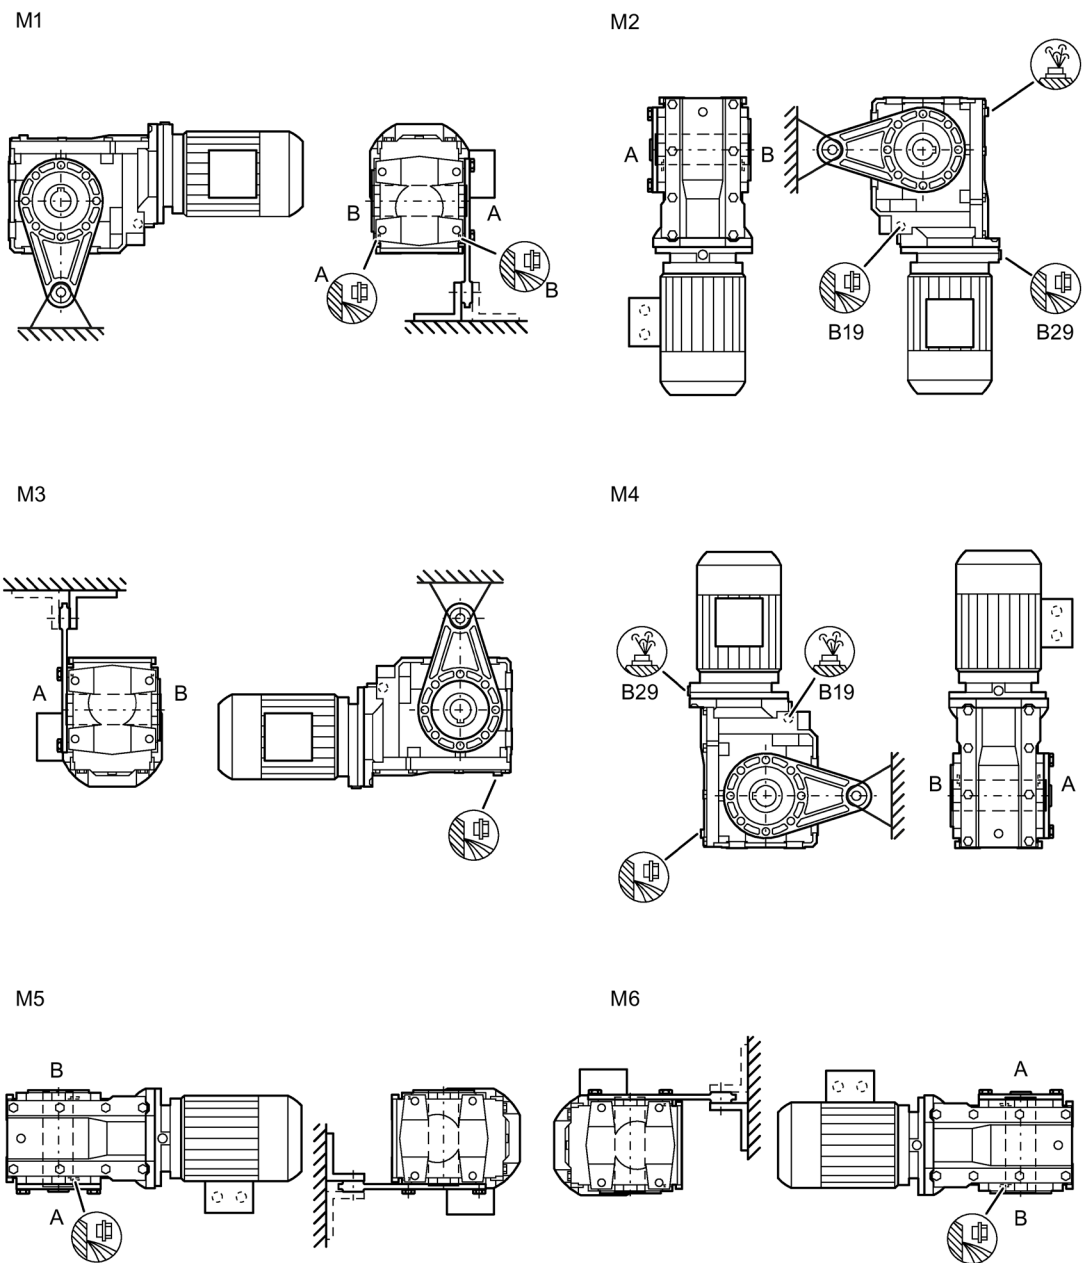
Einbautagen für Kegelradgetriebe BAD Aufsteckausführung Baugrößen 19 - 29
